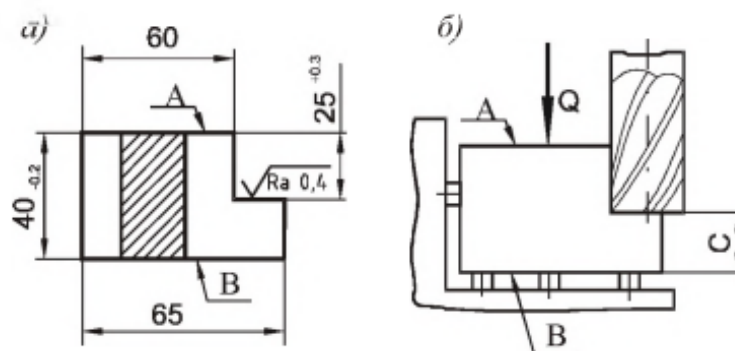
Схемы фрезерования уступа при различных вариантах установки заготовки:
